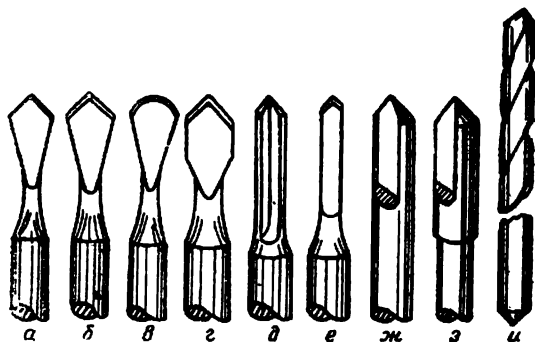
Сверла: *а* - одностороннее перовое сверло; *б* - двустороннее сверло; *в* - сверло для сверления особо жестких металлов; *г* - для коротких точных отверстий; *д* - для выравнивания мягких металлов; *е* - для сверления мягких отверстий в металлах; *ж* - пушечное сверло для отверстий точного диаметра; *з* - для чистовой проходки; *и* - спиральное (американское) сверло
